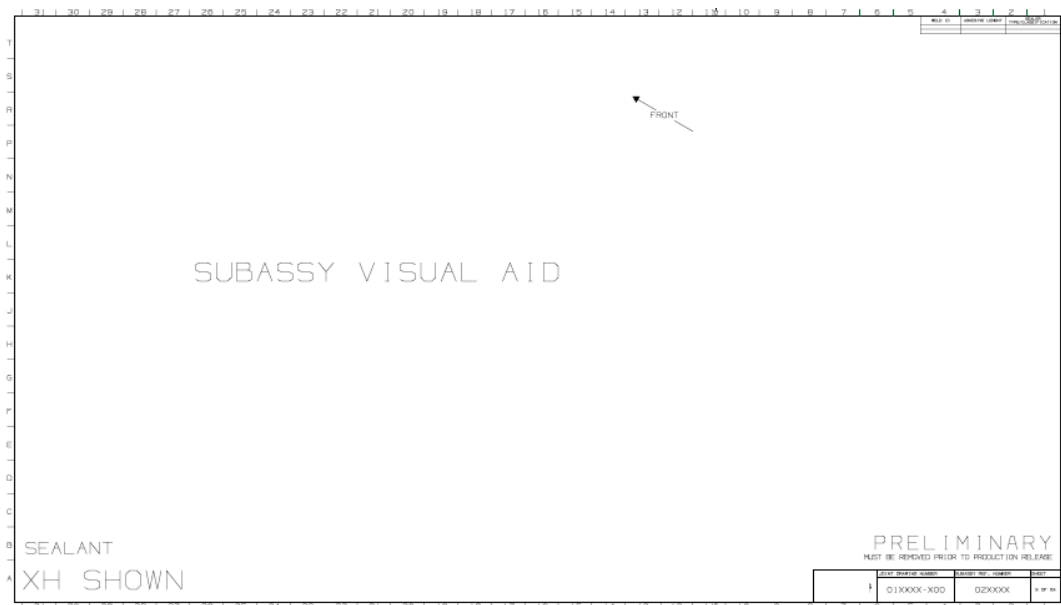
Plantilla de la sección de adhesivos, Dibujo de uniones. [14]
